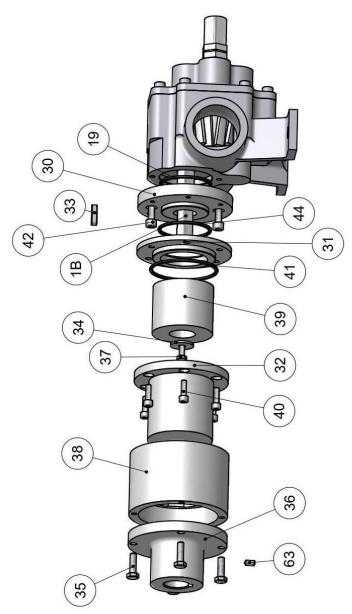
Giunto a Trascinamento Magnetico Figure 5 - Magnetic Drive Coupling
